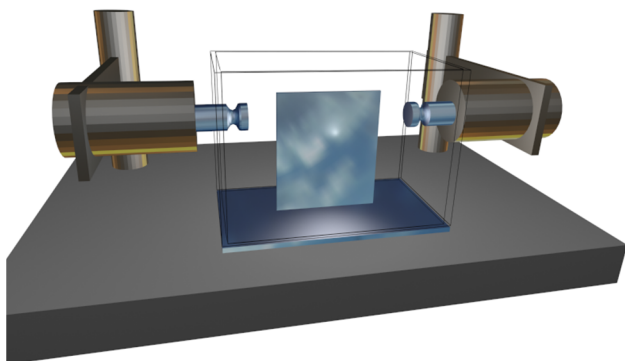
Схема обработки двумя соосно-направленными излучателями
